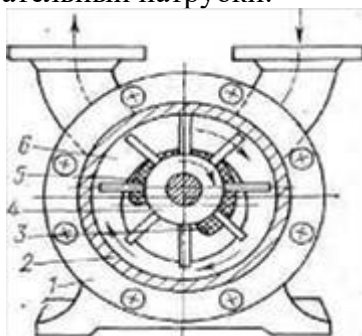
Водокольцевой насос: 1-крышка; 2-корпус; 3-всасывающее отверстие; 4-ротор; 5-нагнетательное отверстие; 6 - водяное кольцо.
